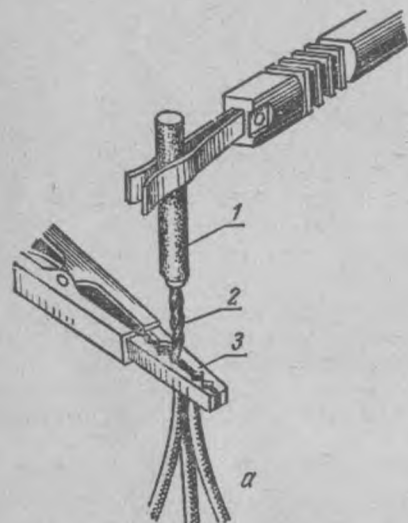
Сварка жил сечением 2,5...10 мм<sup>2</sup>:
